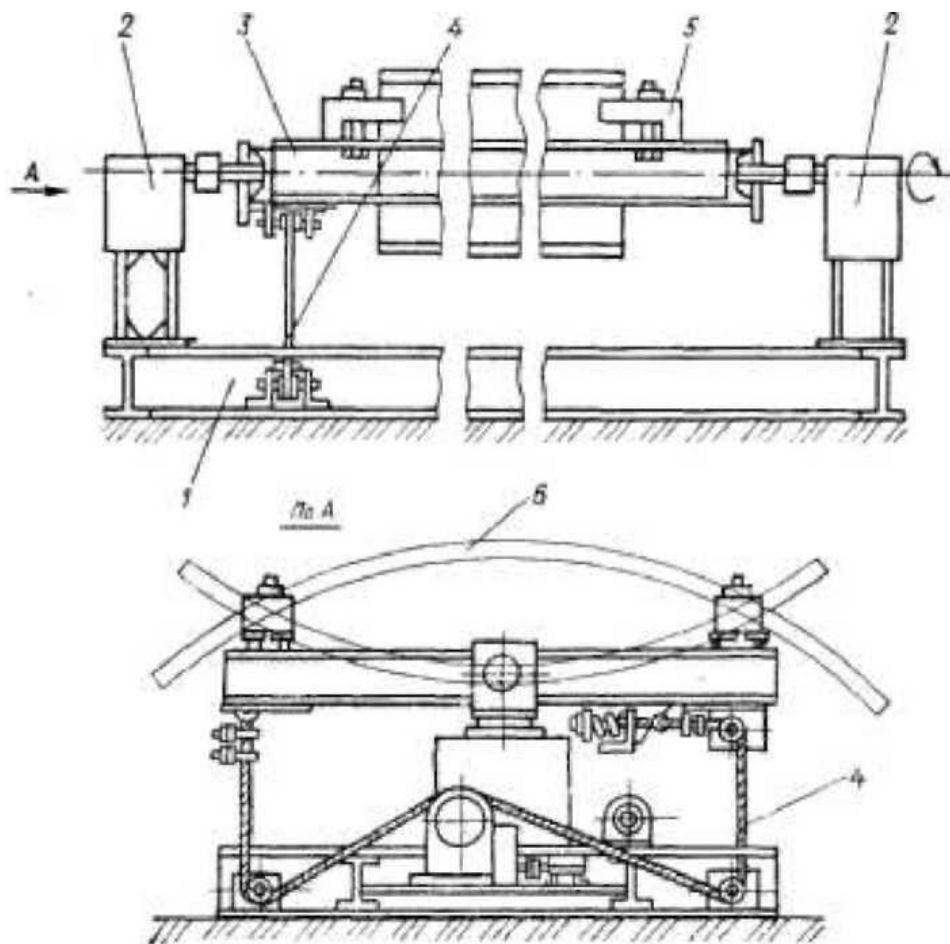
Вращатель для сварки на монтажной площадке укрупнённых блоков кожуха доменной печи
